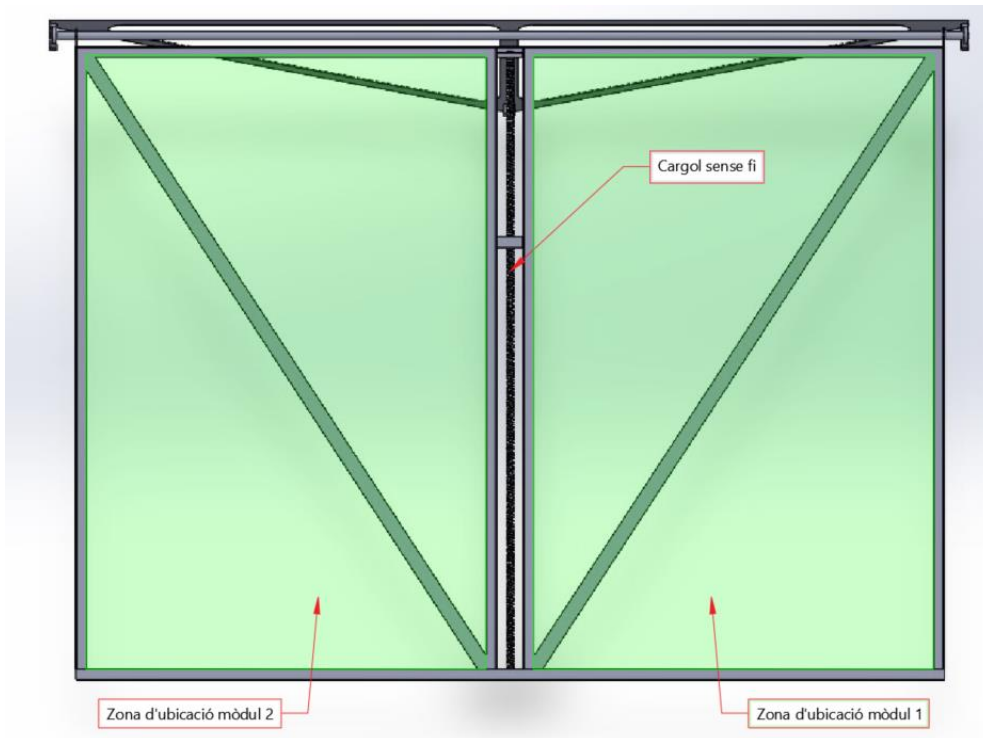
Disseny inicial estructura, vista en planta. Font: pròpia/SolidWorks
